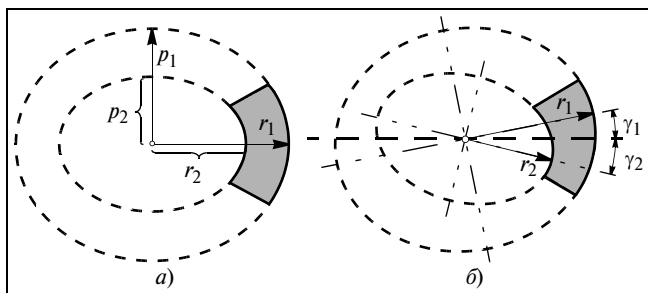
Модель детали Ω_2 с некруговыми (эллиптическими) внешней и внутренней цилиндрическими поверхностями:
